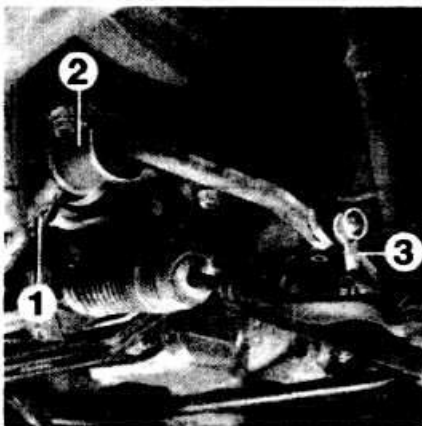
Снятие стабилизатора поперечной устойчивости: 1 — штанга стабилизатора; 2 — кронштейн крепления штанги; 3 — толкающая штанга
